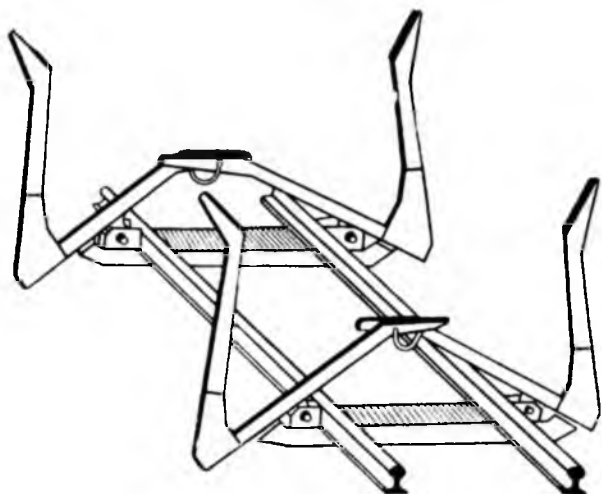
Конструктивная схема шаблона для формирования «шапки» из круглого леса
